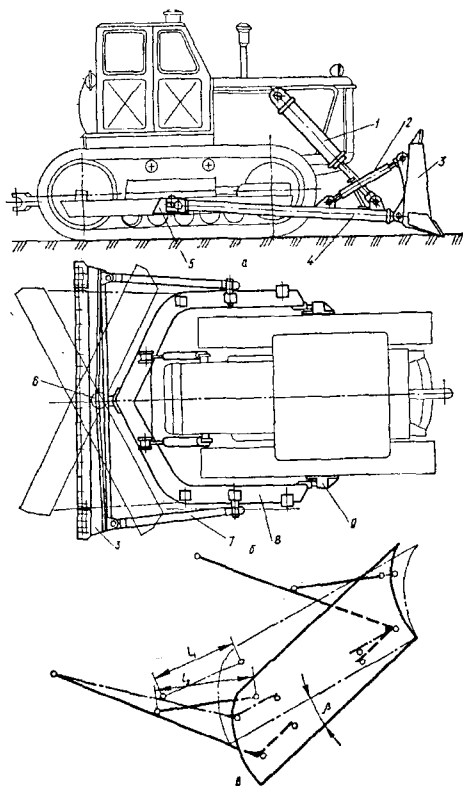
Общий вид бульдозера: а — с неповоротным отвалом;
